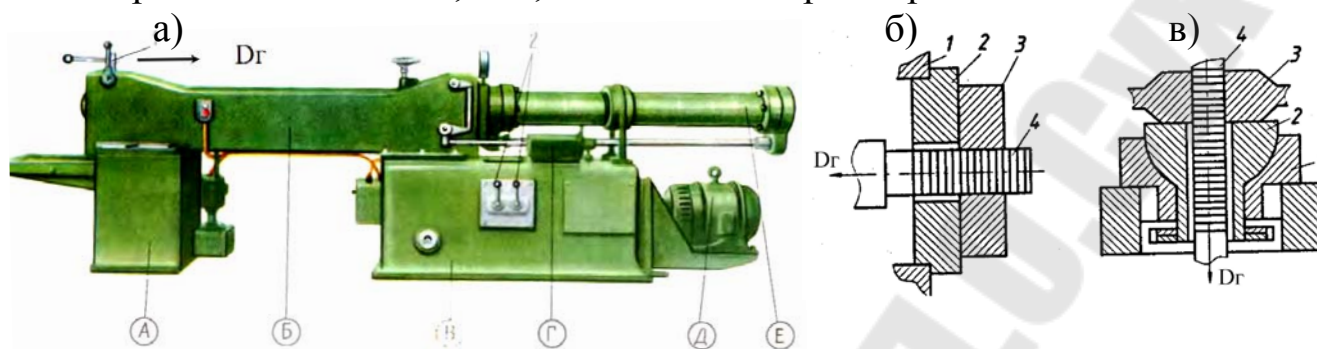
Общий вид горизонтального протяжного станка (а) и схемы протягивания отверстий (б, в)
